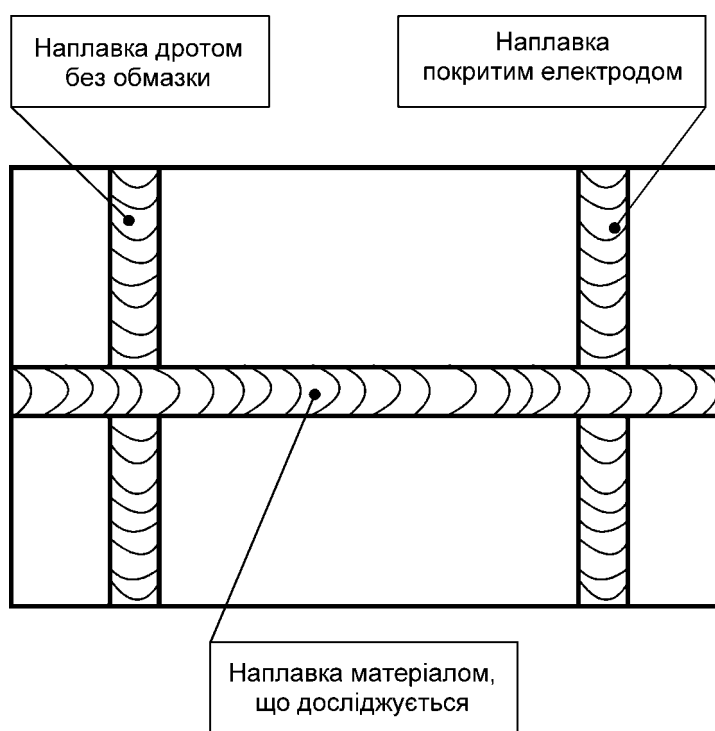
Зразок з наплавками, що імітують прихватки [2]
